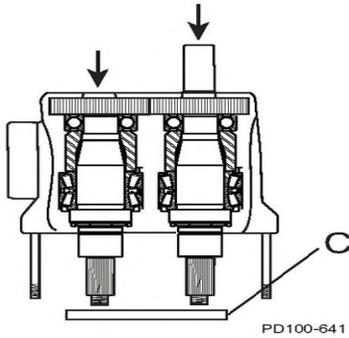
Herausdrücken der Wellen aus dem Getriebegehäuse
